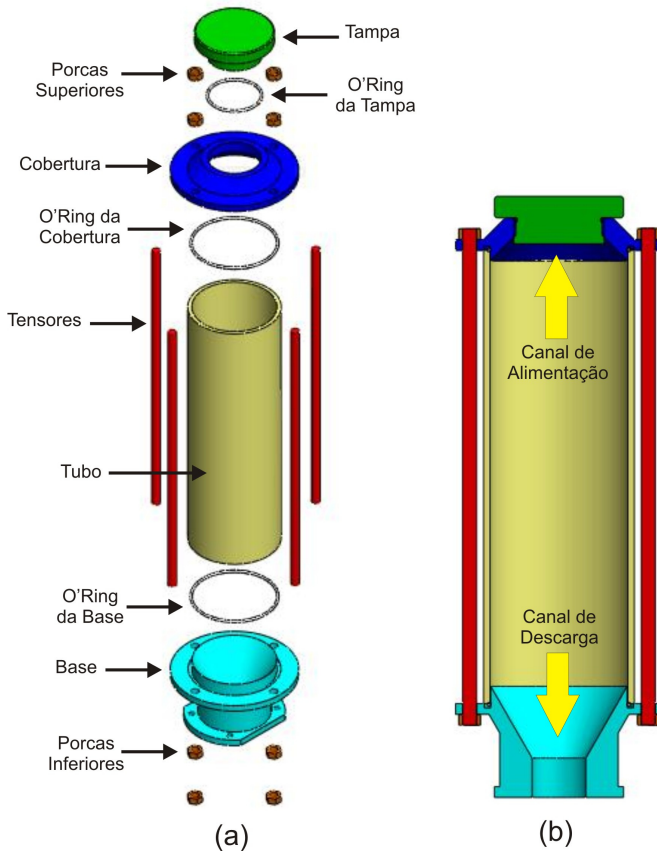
Desenho do Silo em ambiente CAD: a) vista explodida da estrutura; b) estrutura em corte frontal com principais canais
